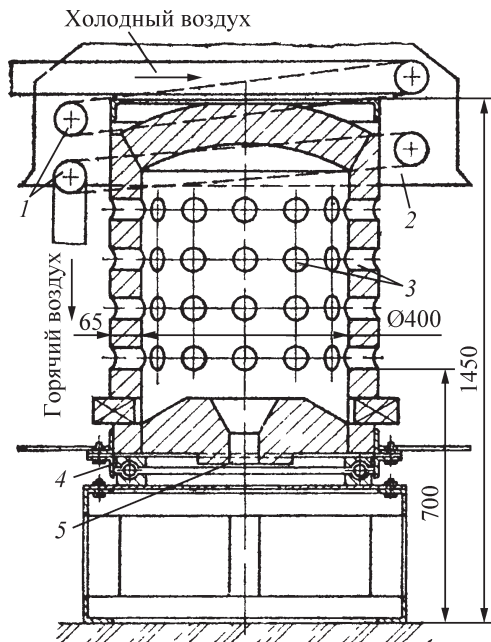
Очковая вращающаяся печь для нагрева концов заготовок при штамповке гаек и высадке головок болтов и заклепок:
